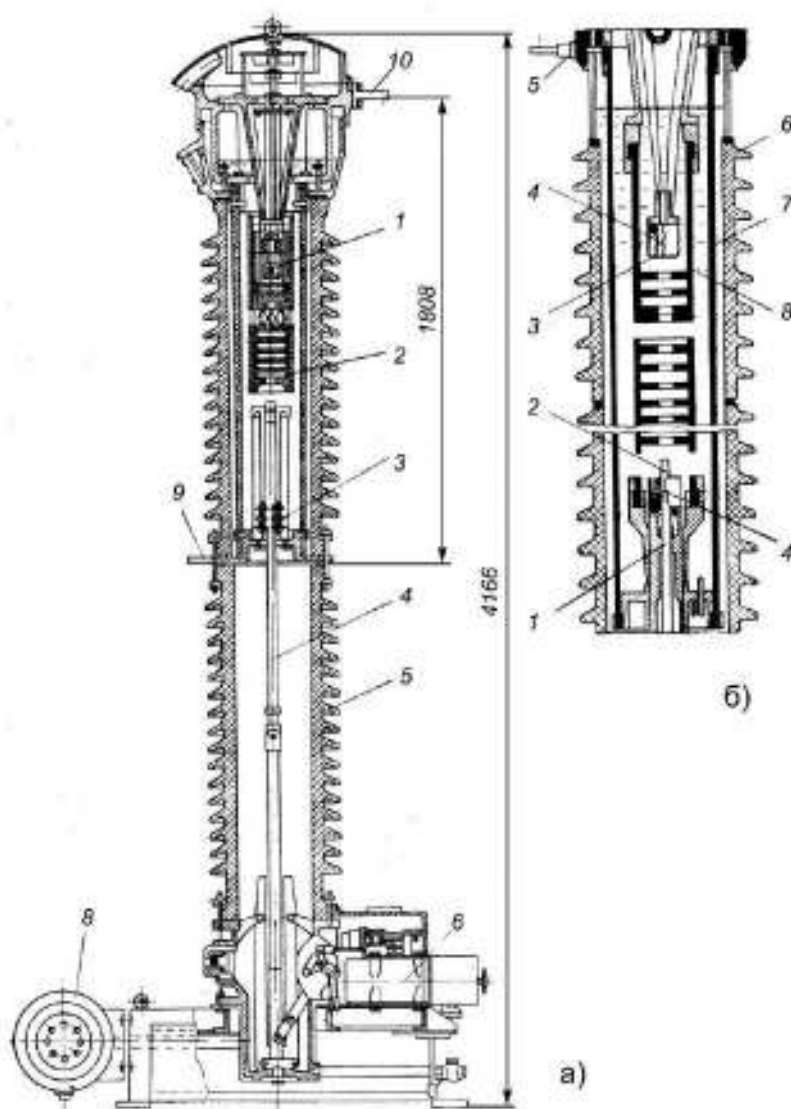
Выключатель ВМК-110: а) – разрез одного полюса выключателя: 1 – неподвижный розеточный контакт; 2 – гасительная камера; 3 – роликовый токосъемный контакт; 4 – подвижной контактный стержень; 5 –
